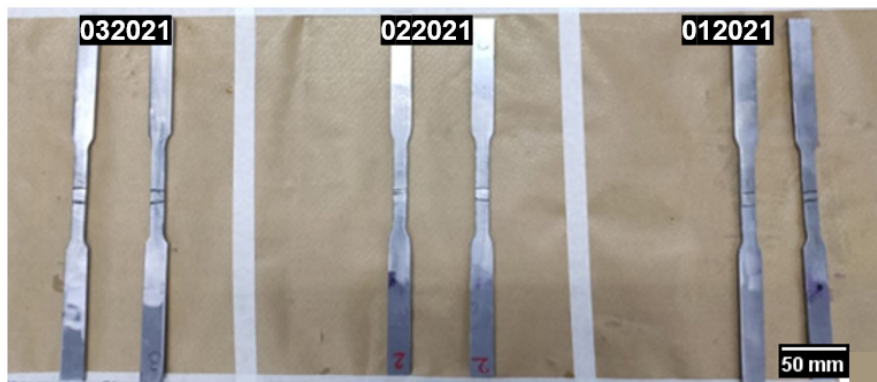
Amostras soldadas preparadas para realização do ensaio de tração, 02 para cada aporte térmico. Fonte: Autor.
